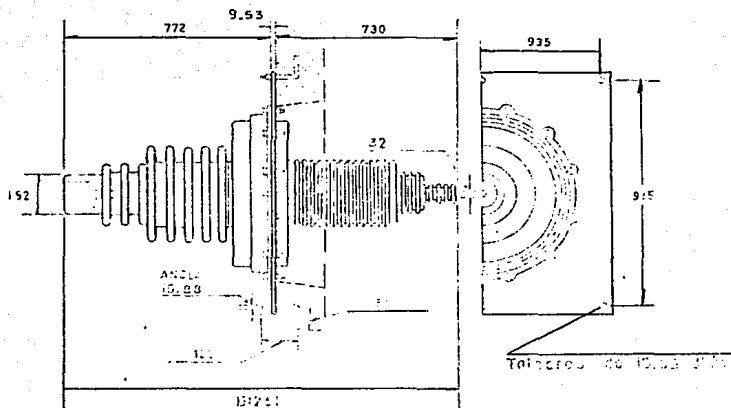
Aislador Tipo Pasamuro (Clase 58-1)
